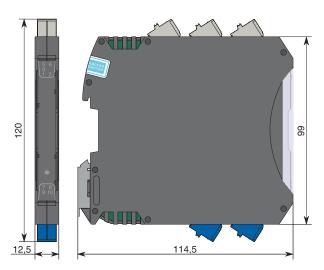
Габаритные размеры барьера в корпусе шириной 12,5 мм с разъемами с пружинными клеммниками и тестовыми гнездами
